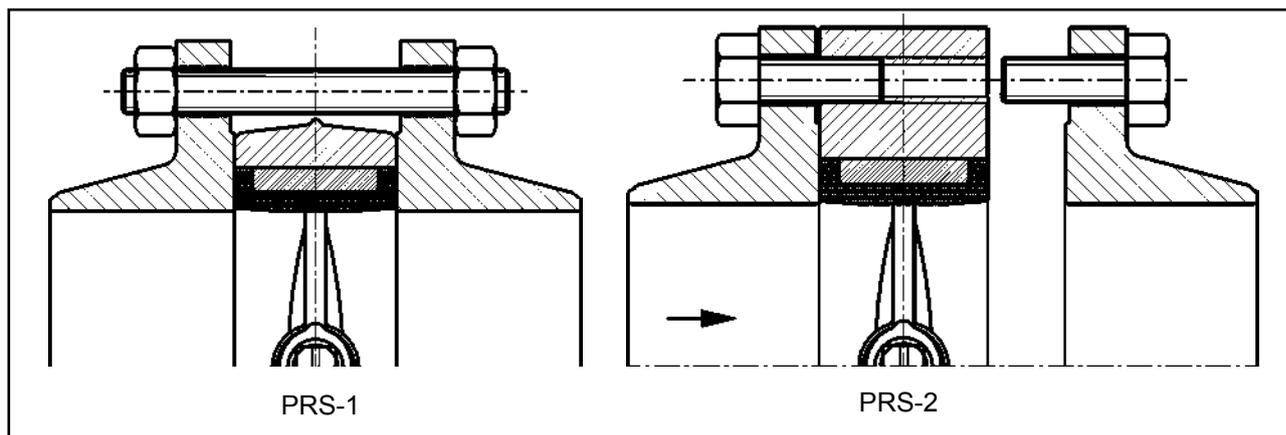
Монтаж дроссельной заслонки в трубопроводе
